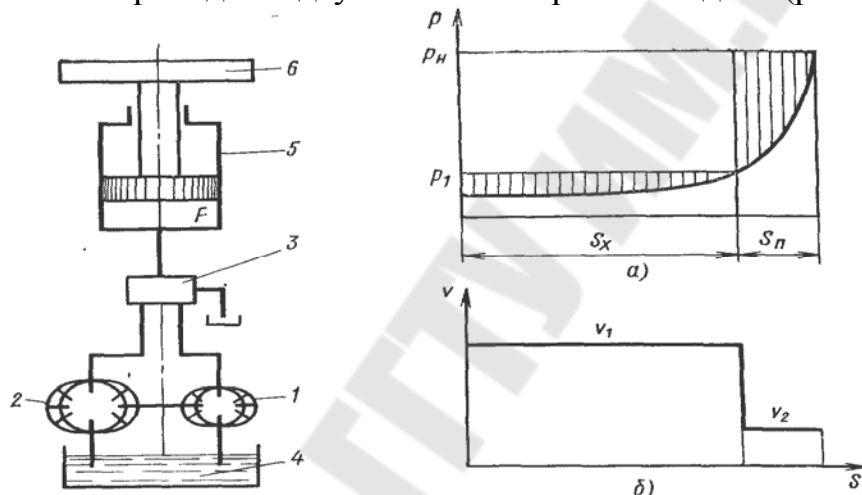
Схема гидропривода прессовой формовочной машины с двумя насосами:
